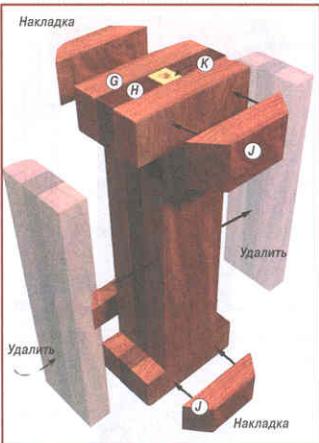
Клееный блок — заготовка для ножки. Чтобы облегчить обработку на токарном станке, фрагменты, указанные стрелками, вырезают на ленточной пиле.
